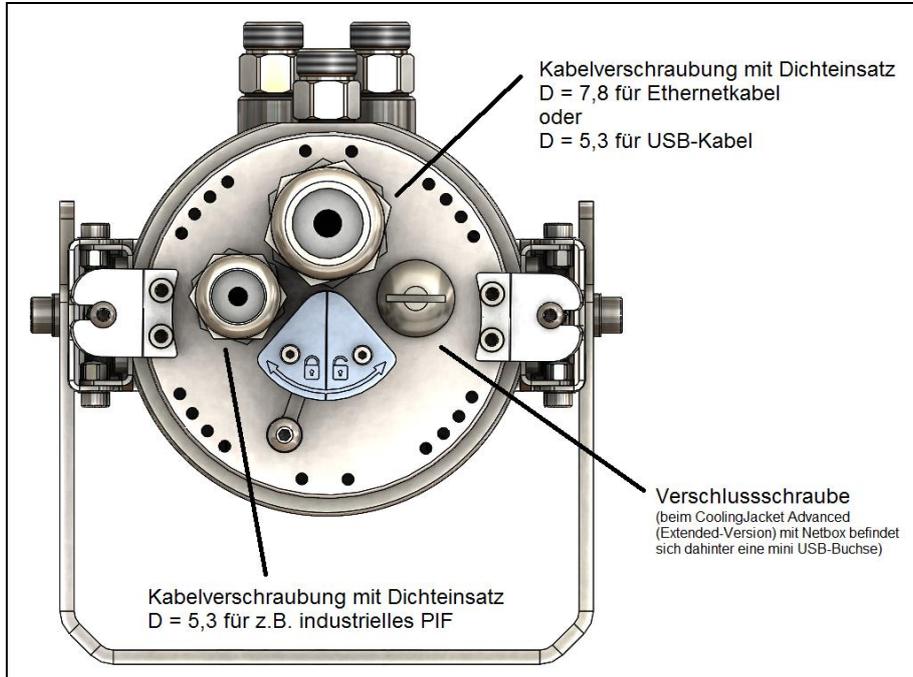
Kabelverschraubungen mit Dichteinsatz
